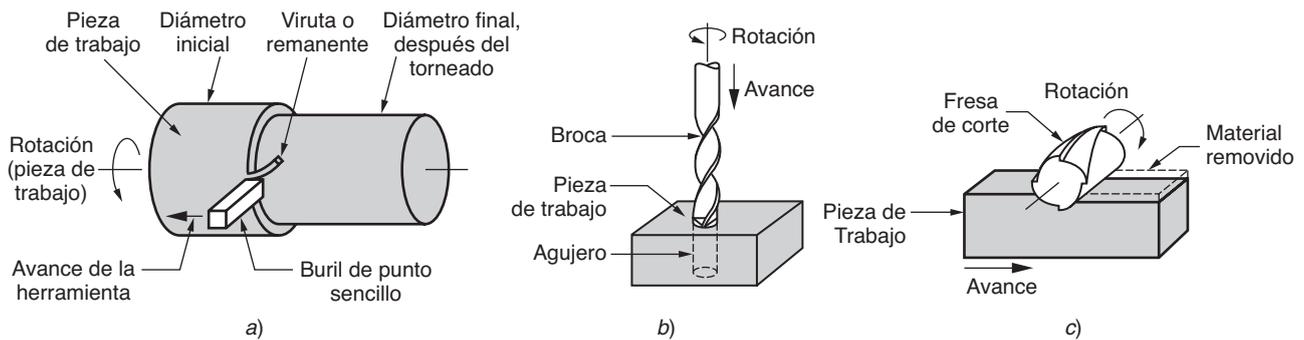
Operaciones comunes de maquinado: a) torneado, en el que una herramienta de corte de un filo retira metal de una pieza de trabajo que gira, a fin de reducir su diámetro; b) taladrado, en la que una broca en rotación avanza dentro de la pieza de trabajo, con lo que crea un agujero redondo; y c) fresado, en la que una pieza de trabajo se hace avanzar por un cortador giratorio con filos múltiples.
